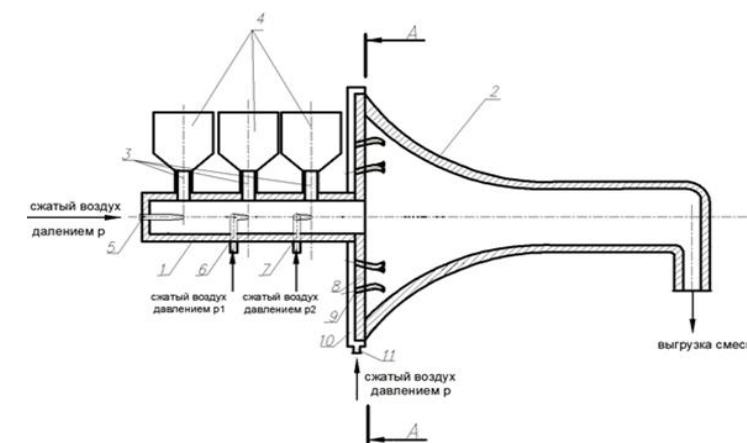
Пневмосмеситель непрерывного действия: 1 – подающая труба; 2 – корпус основной камеры смешения; 3 – патрубки ввода компонентов; 4 – загрузочные бункера; 5, 6, 7 – сопла дополнительные; 8 – торец; 9 – сопла; 10 – крышка; 11 – патрубок подвода сжатого воздуха
